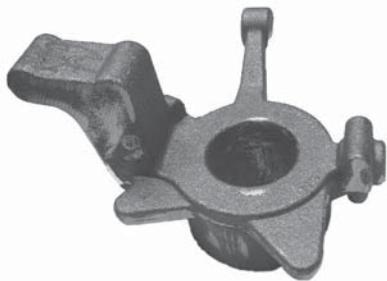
Отливка «Кулак поворотный» мод. ВАЗ-2116
